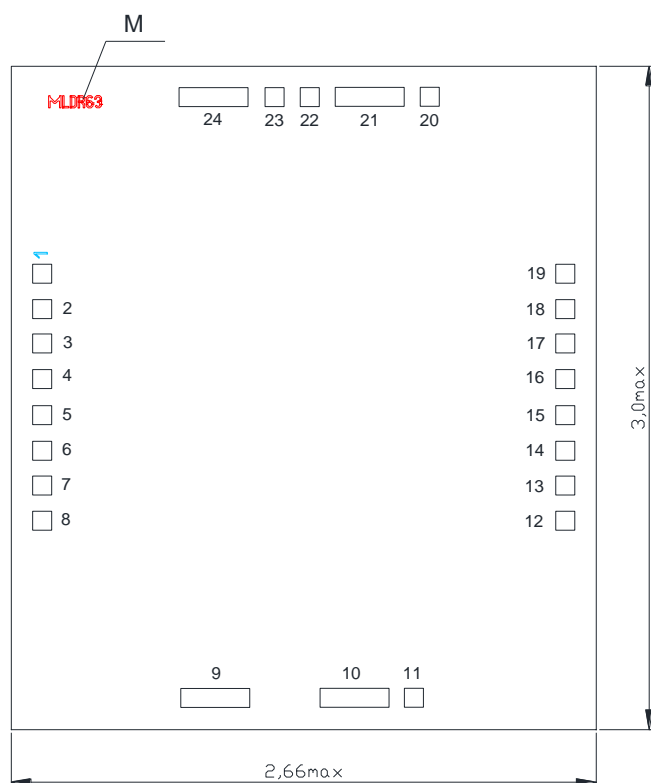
Габаритный чертёж микросхемы в корпусе Н06.24-1В
